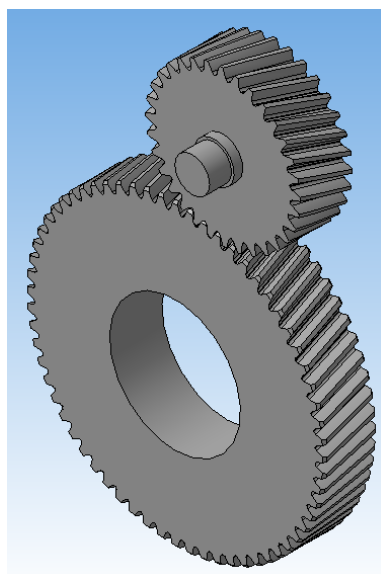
Зубчатое зацепление проектированное с помощью модуля SHAFT 3D
